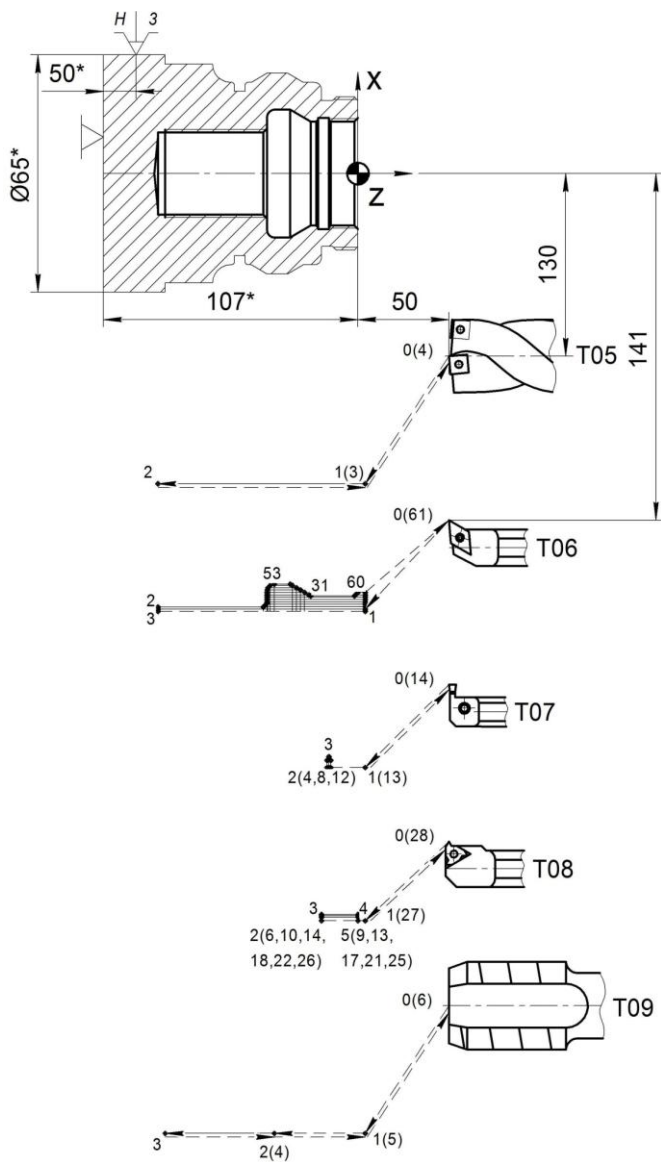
Траектории движения инструментов при внутренней обработке (размеры обрабатываемых поверхностей не показаны)
